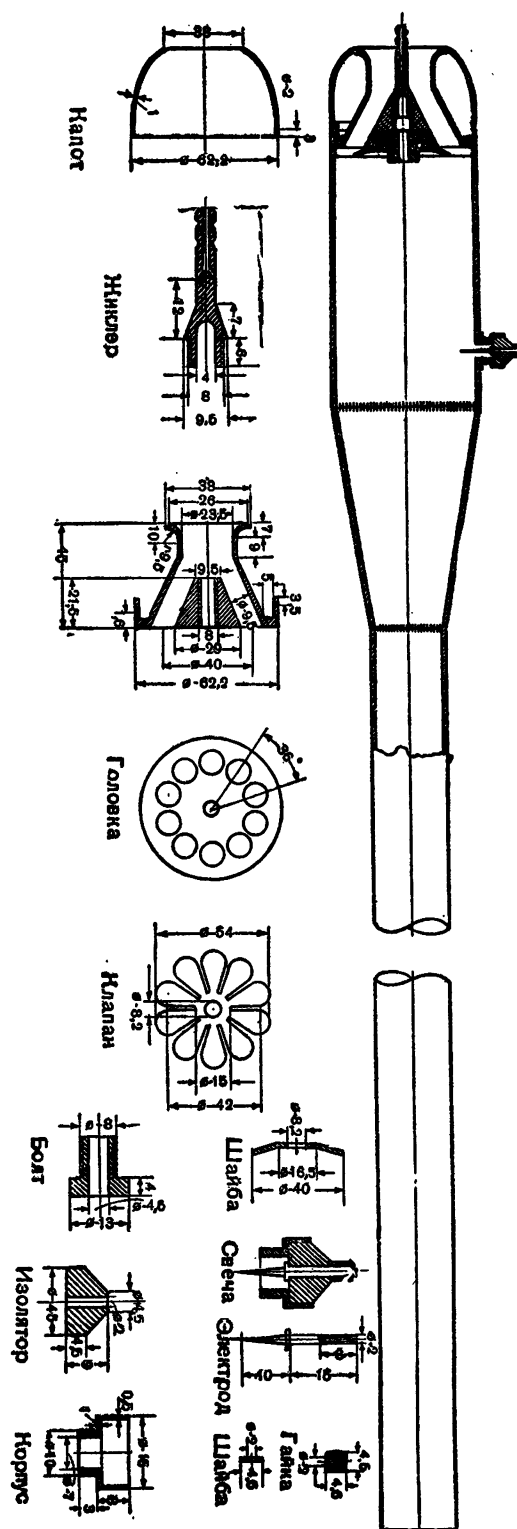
Реактивный двигатель для моделей судов (ПВРД).
